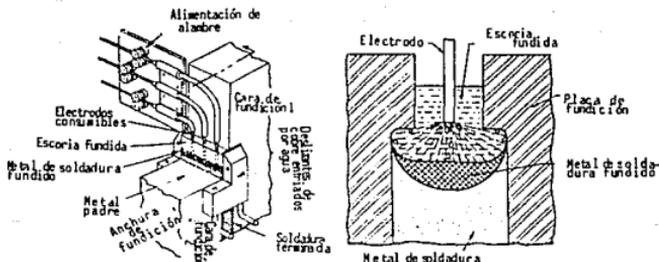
(izq.) Arreglo de equipo y trabajo para hacer una soldadura vertical mediante el proceso de electroescoria.
